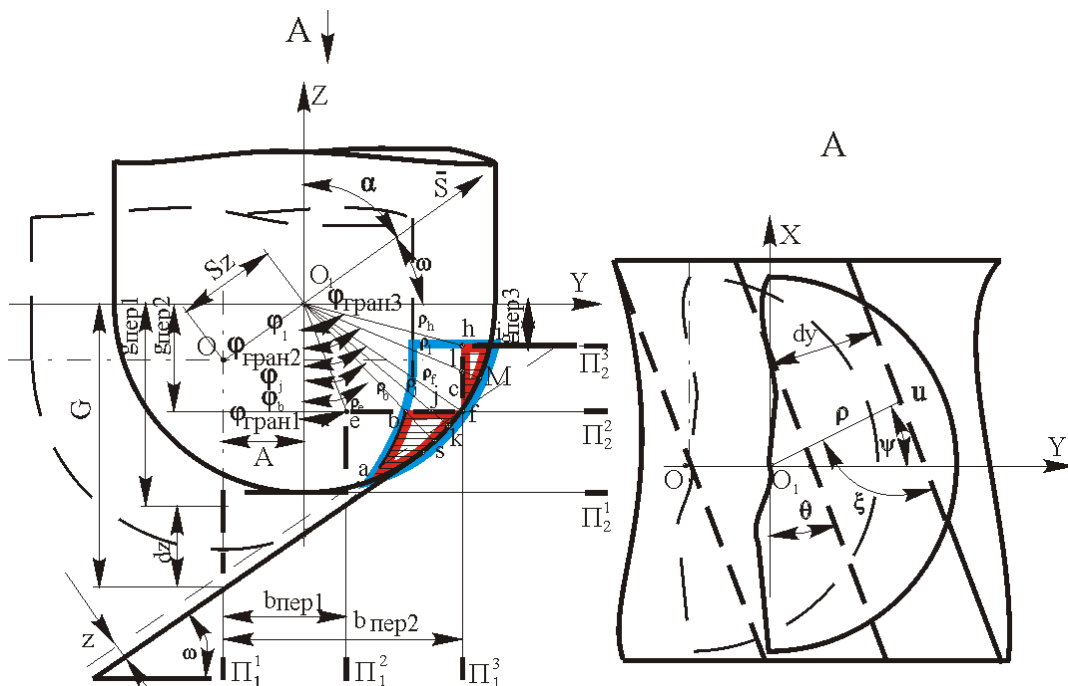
Геометрія шару, що зрізується, при обробці сферичною кінцевою фрезею
